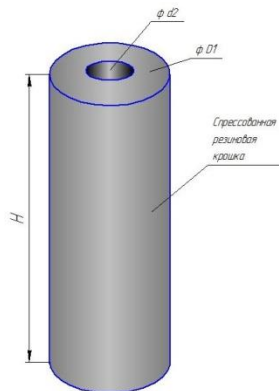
Деталь 2 – полый цилиндр из спрессованной резиновой крошки
